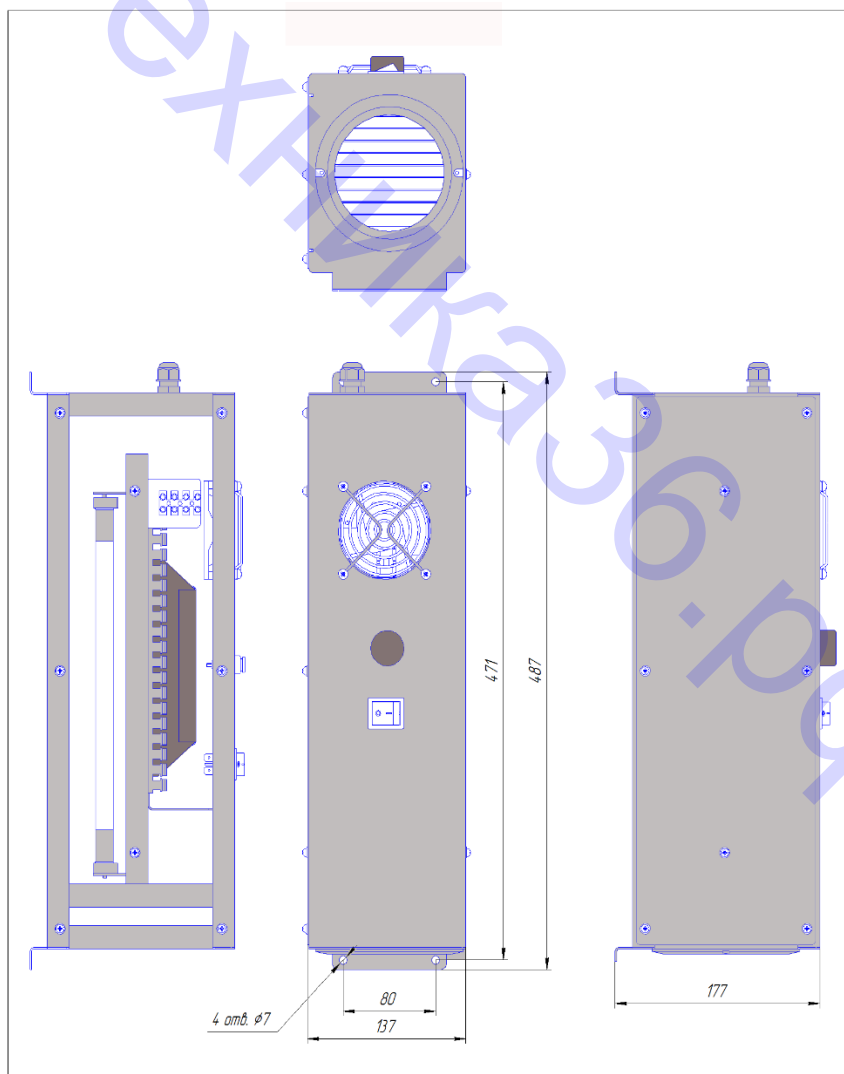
УОВ-3м-18А. Габаритный чертеж
